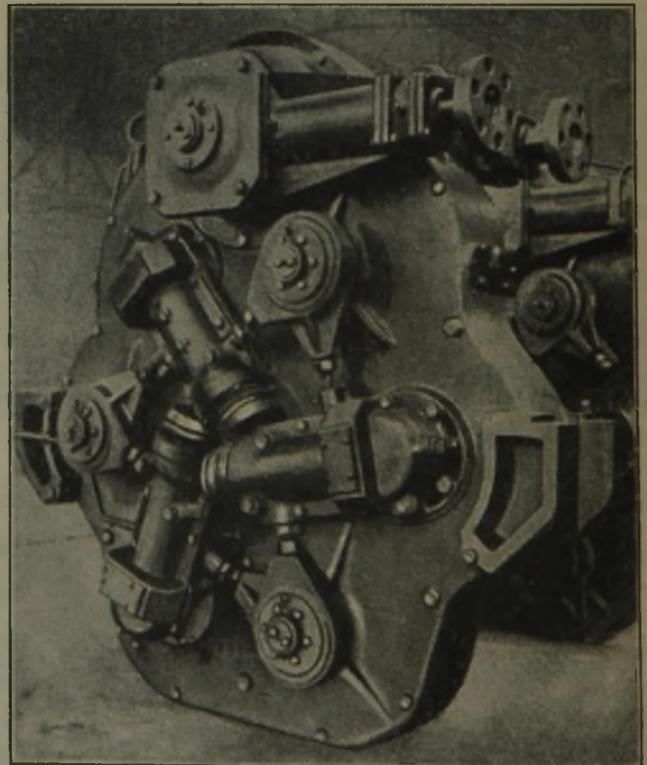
Rohrreduzierwalzwerksgerüst. Ansicht auf einen Walzensatz.
